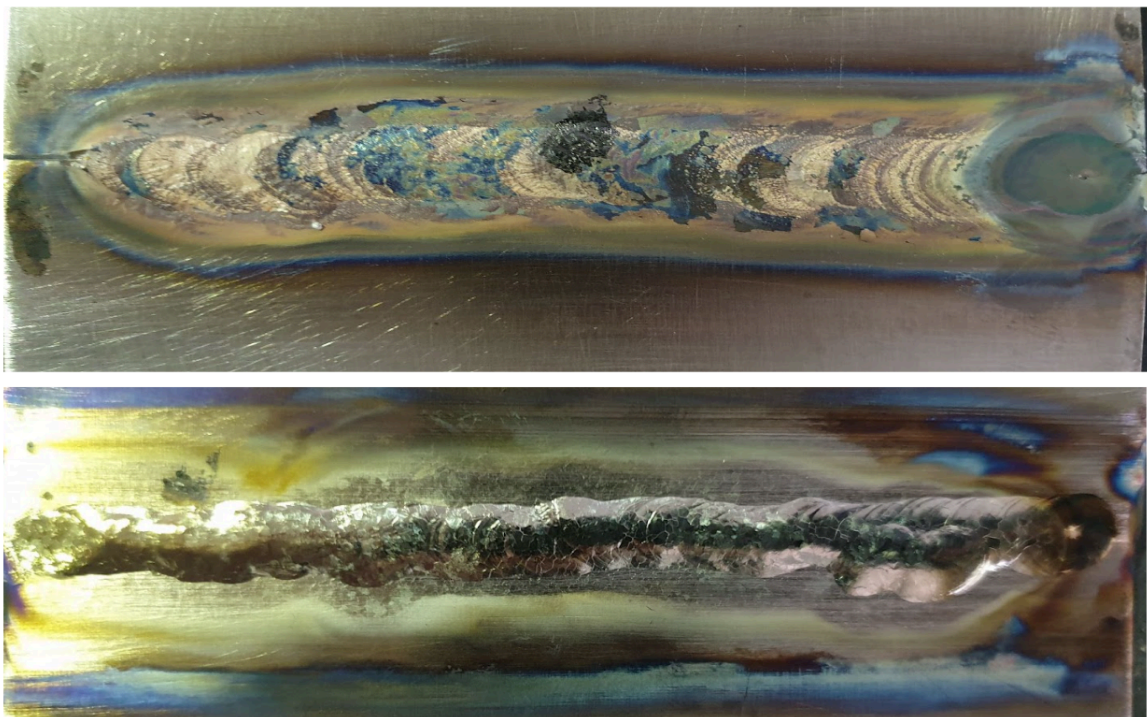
Echantillon 05 (soudure avec un courant continu)
